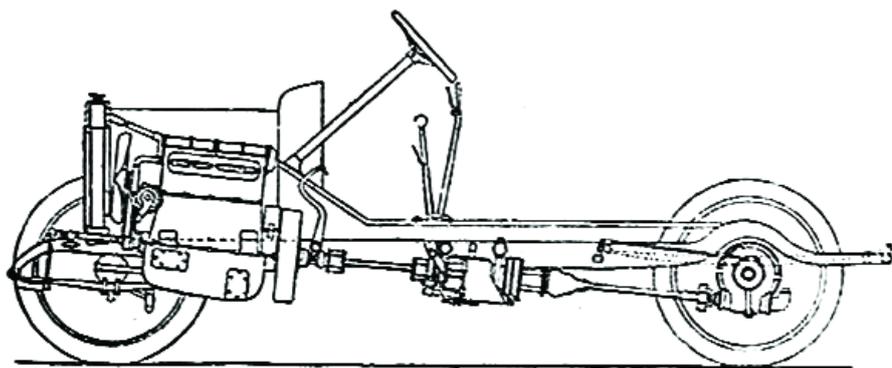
Шасси 12-сильного автомобиля конструкции Даймлера
